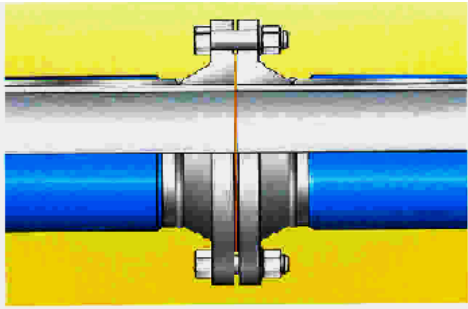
Îmbinarea prin flanșă cu gât sudată pe țevă
